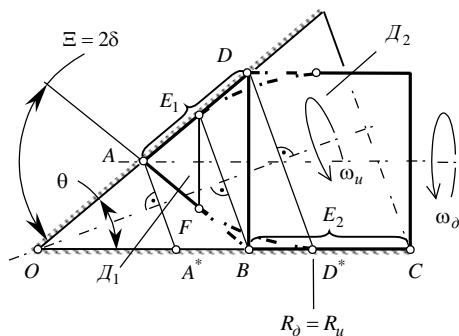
Формообразование цилиндрического и конического участков поверхности детали поверхностью внутреннего конуса.
